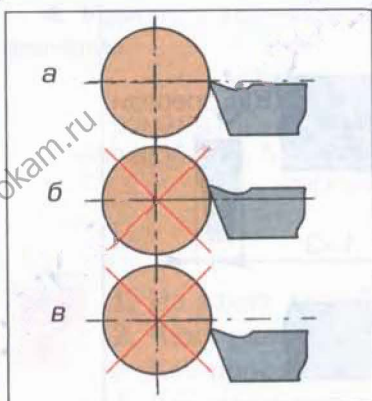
Установка отрезного резца: а – правильно; б, в – неправильно
